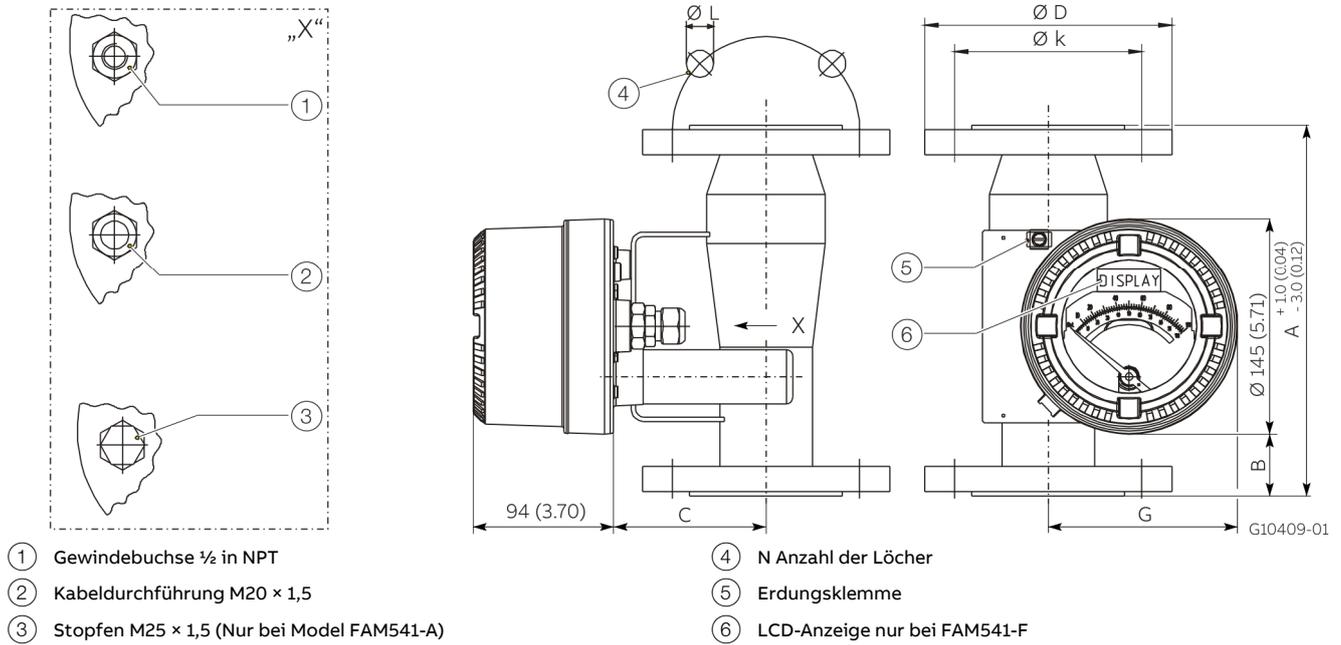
Abmessungen für Flanschgeräte in mm (in), Toleranzen ±2 mm
